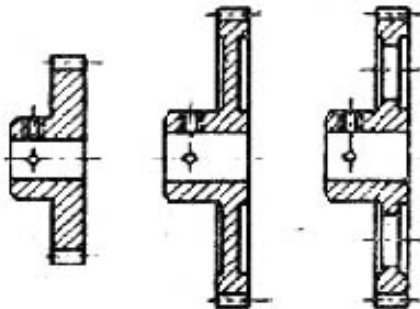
Типовые конструкции цилиндрических колёс
